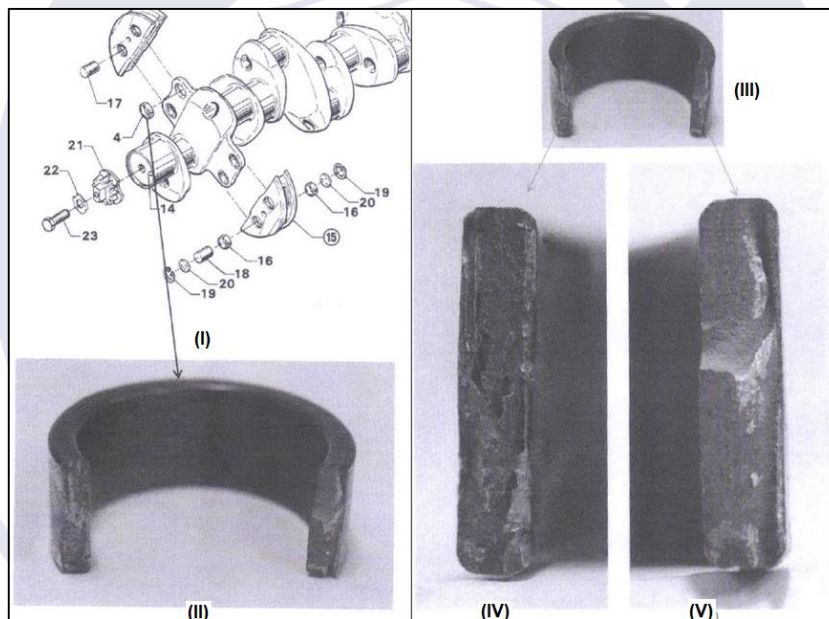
(I) visão explodida dos componentes do virabrequim e seus elementos.
